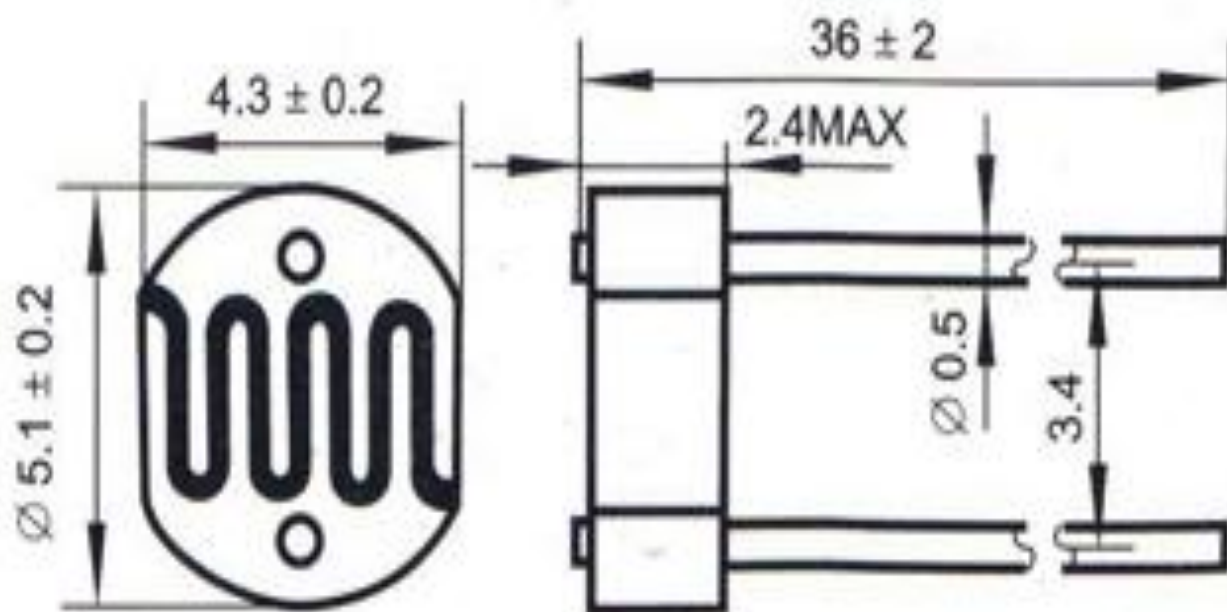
Габаритні розміри фоторезистора GL5516
